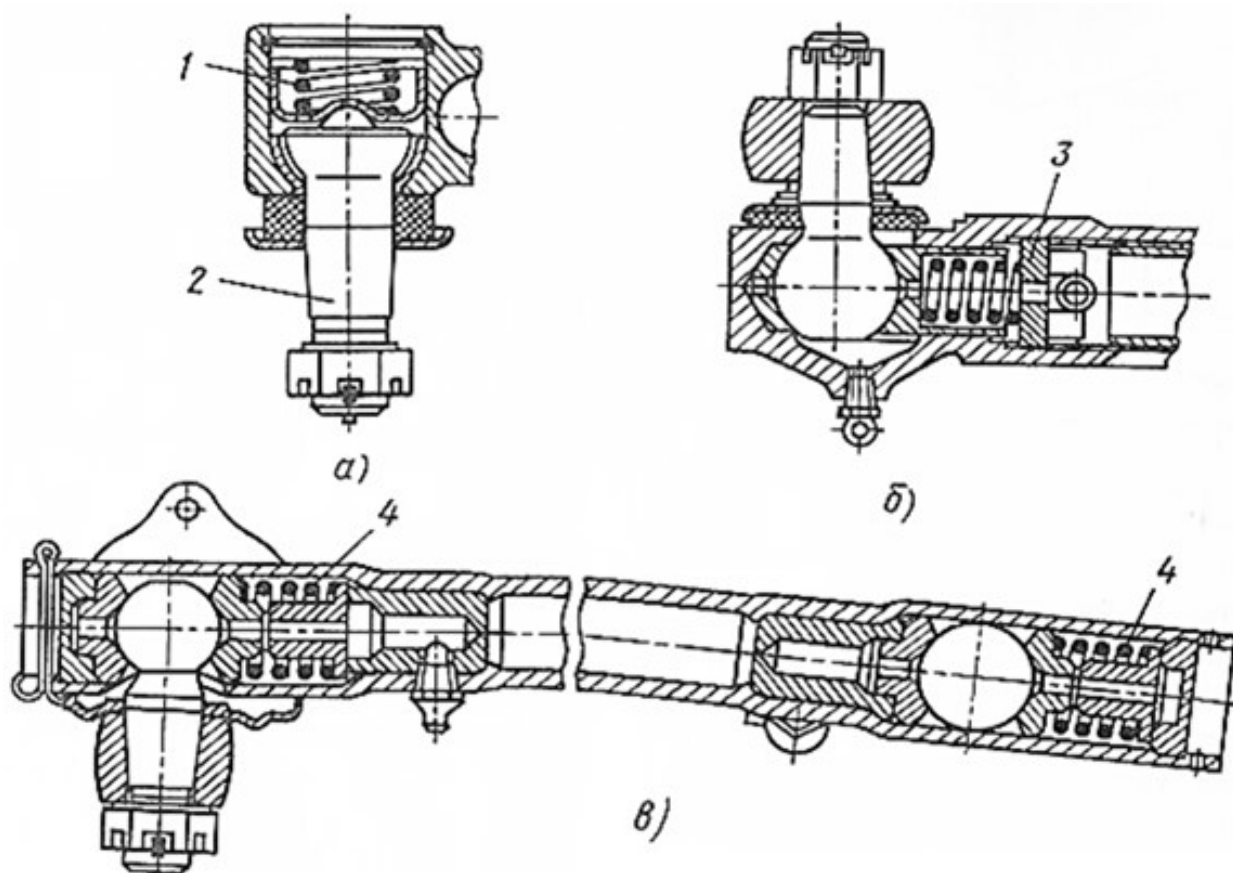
Конструкция шарниров рулевых тяг
